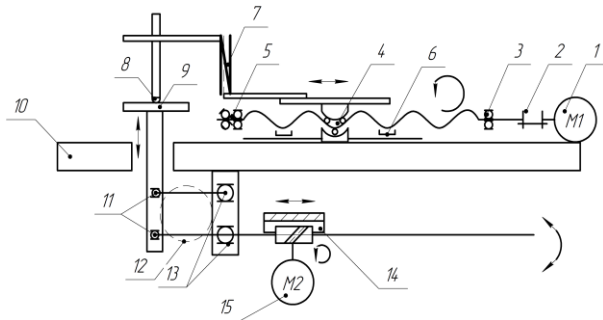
Принципиальная кинематическая схема: 1- Двигатель шаговый; 2-Муфта ; 3-Подшипниковый узел; 4- Передача винт-гайка; 5-Подшипниковый узел; 6-Линейные подшипники качения; 7-Датчик силы; 8-Индентор; 9- Образец; 10-Основание; 11-Подшипники качения; 12- Пантограф; 13-Подшипниковый узел; 14-Реечная передача; 15-Двигатель шаговый.
